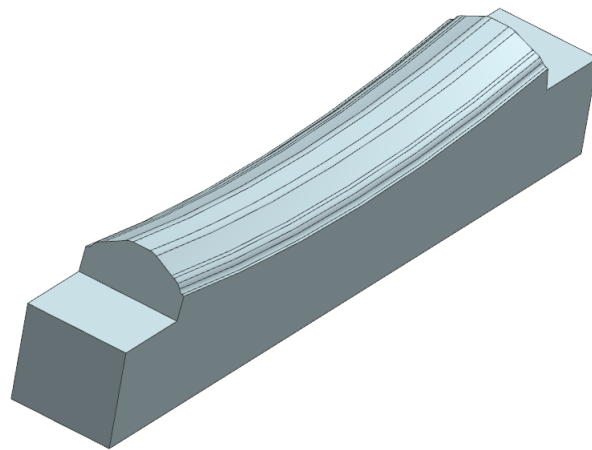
Molde Interior. Diseño del molde interior. (Fuente: Propia)
